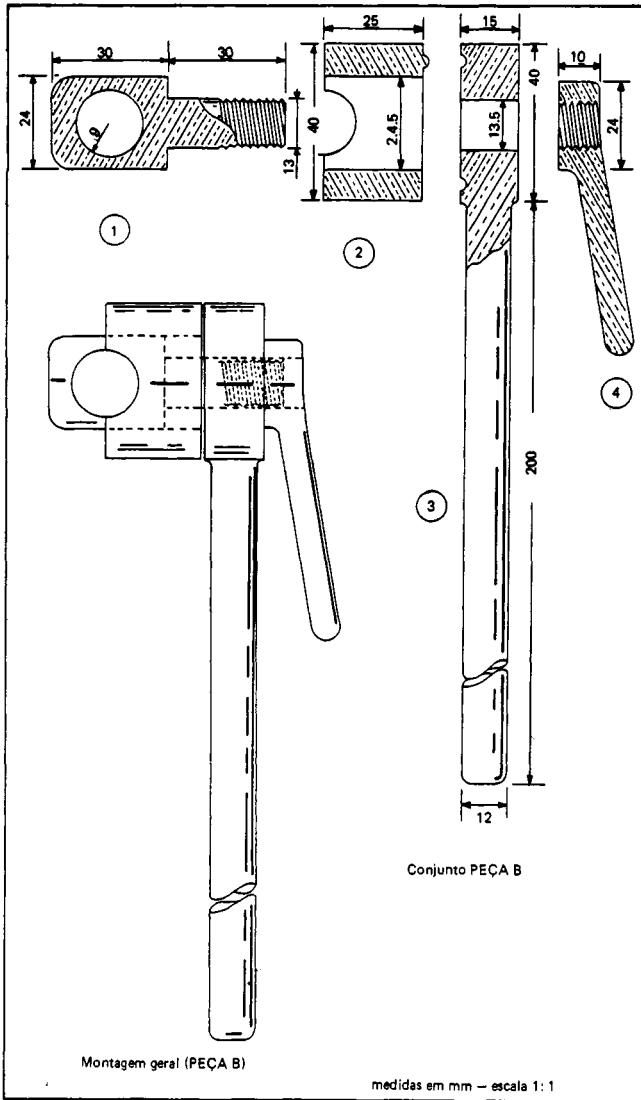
Esquema geral da peça B e destaque do conjunto de fixação.
